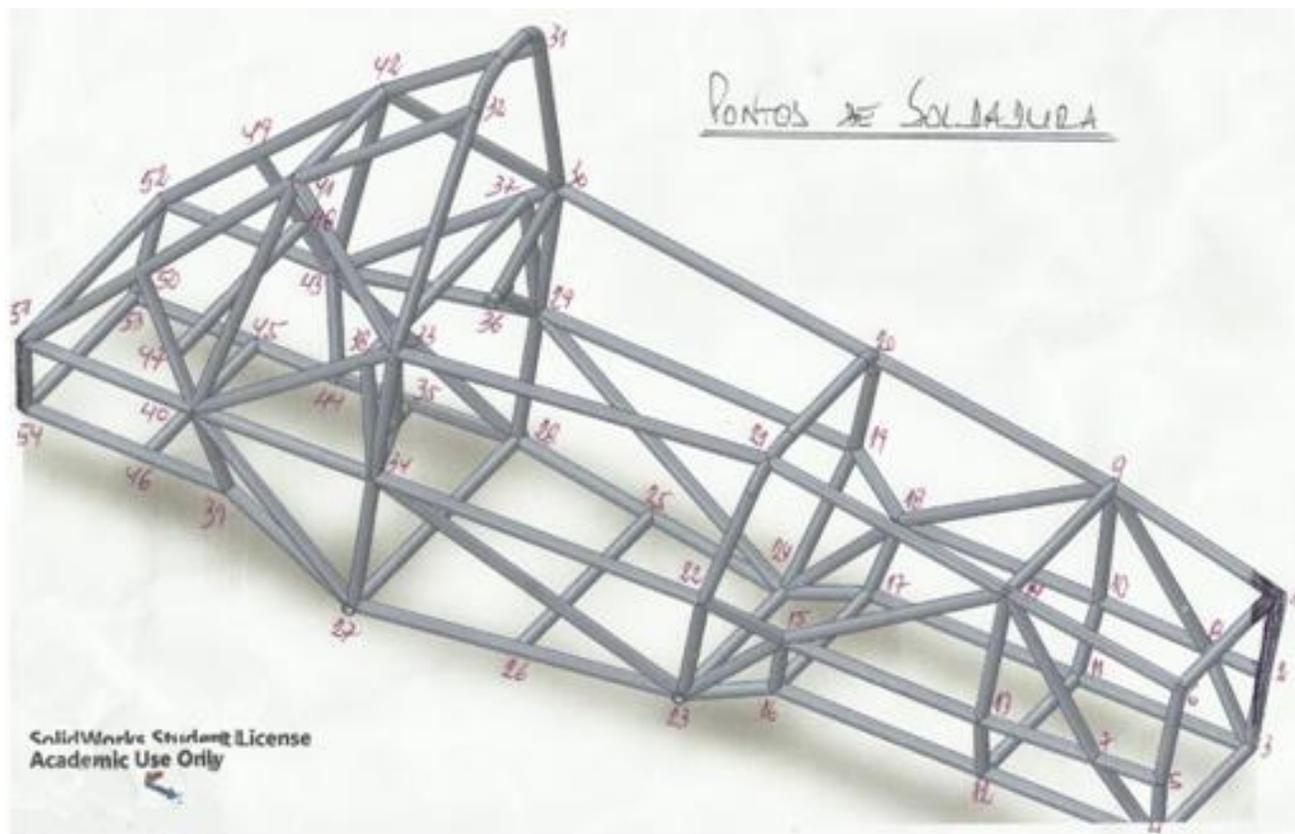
Identificação dos Pontos de Soldadura do Chassis do Veículo do FSIPLeiria
